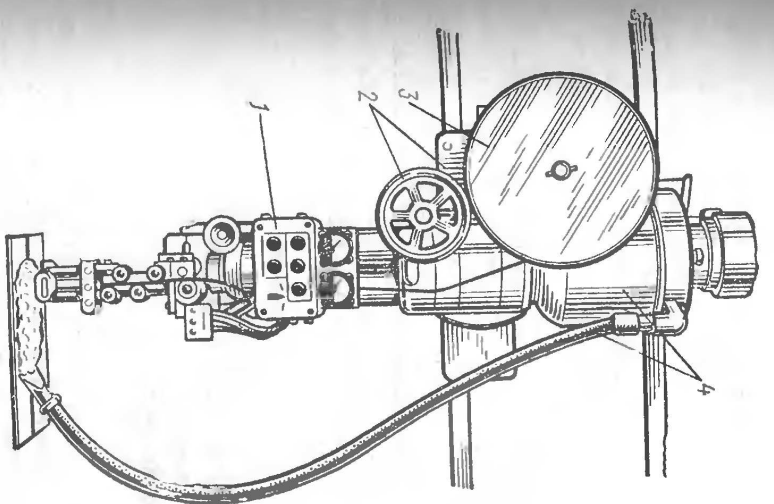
Подвесной автомат для дуговой сварки:
